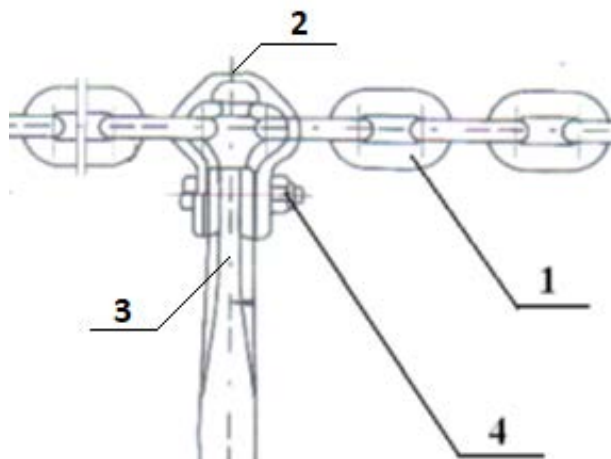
Фрагмент скребковой цепи в сборе: 1 - звено цепи круглое; 2 - звено соединительное; 3 - скребок; 4 - соединительный крепёж
